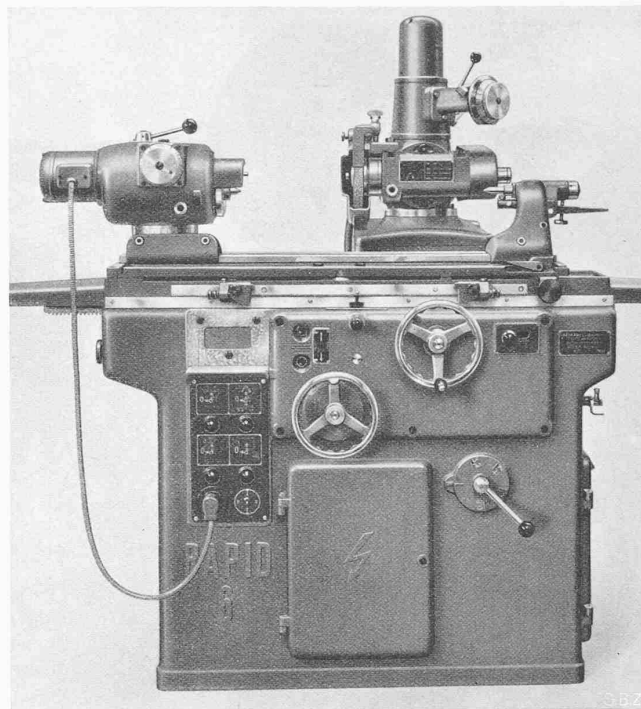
Universal-Werkzeug-Schleifmaschine der «Rapid» A. G. Uster
